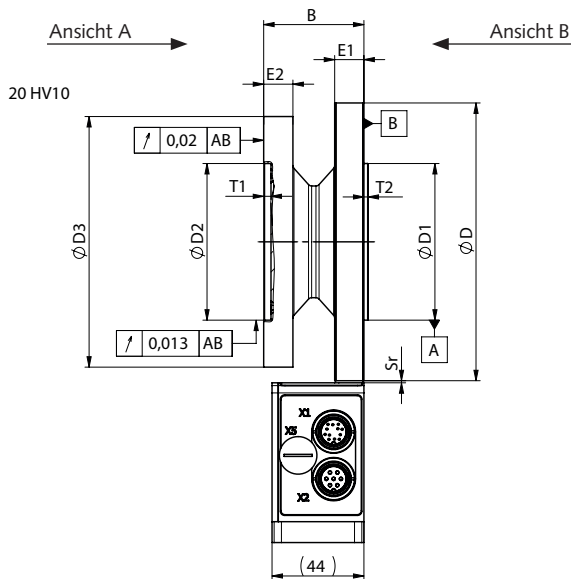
Maßzeichnung Seitenansicht KiTorq System
